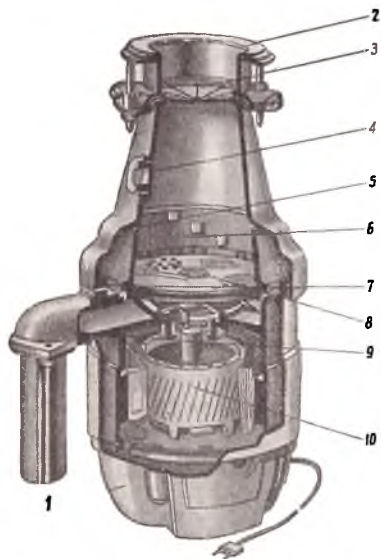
Электрическая мусородробилка бытовая: 1 — корпус; 2 — загрузочное отверстие; 3 — резиновая диафрагма; 4 — отверстие для подключения спускного шланга посудомойки; 5 — дробильная камера; 6 — дробильные ножи; 7 — дробильный диск; 8 — сетка дробильного диска; 9 — спускной патрубок; 10 — ротор электродвигателя
